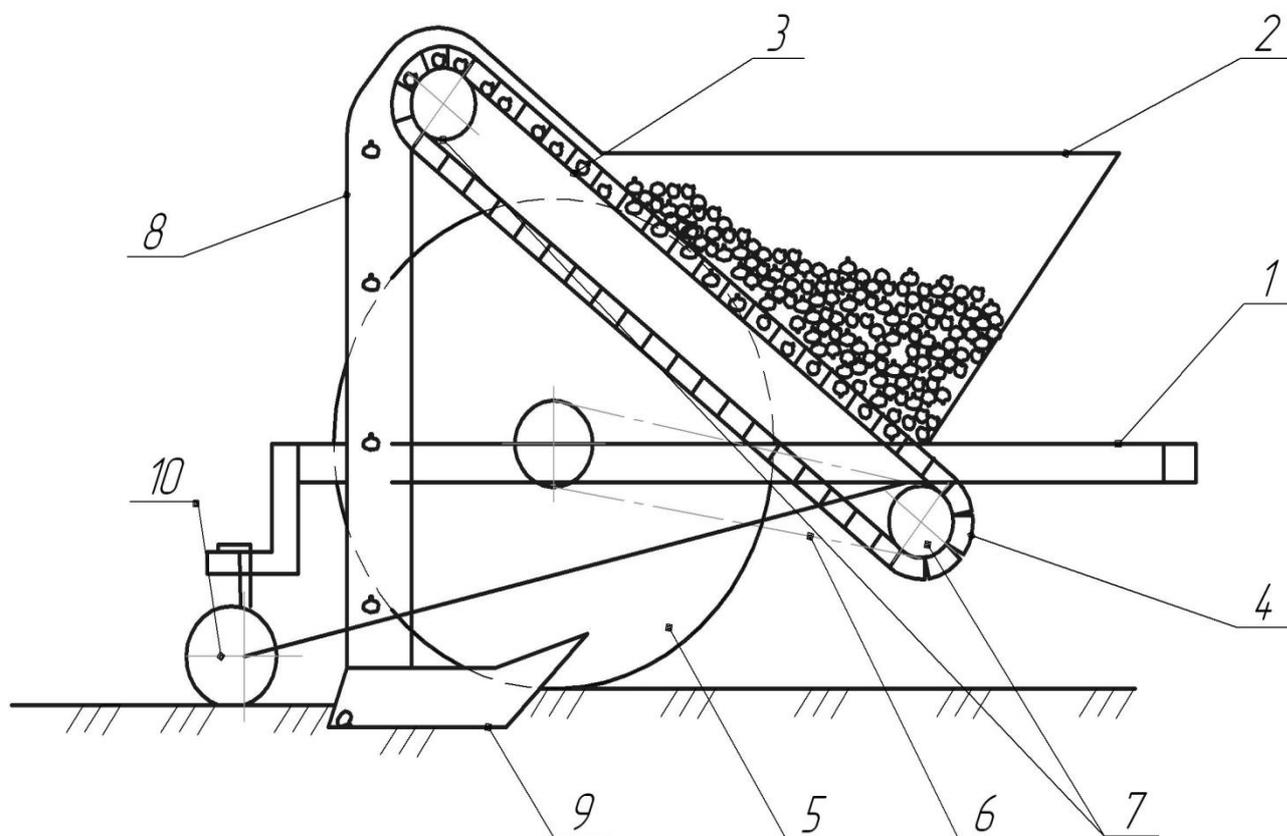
Схема ячеисто-ленточного высаживающего аппарата: 1 – рама; 2 – бункер; 3 – лента; 4 – ячейки; 5 – опорно-приводное колесо; 6 – привод; 7 – шкив; 8 – семяпровод; 9 – сошник; 10 – прикатывающие катки
